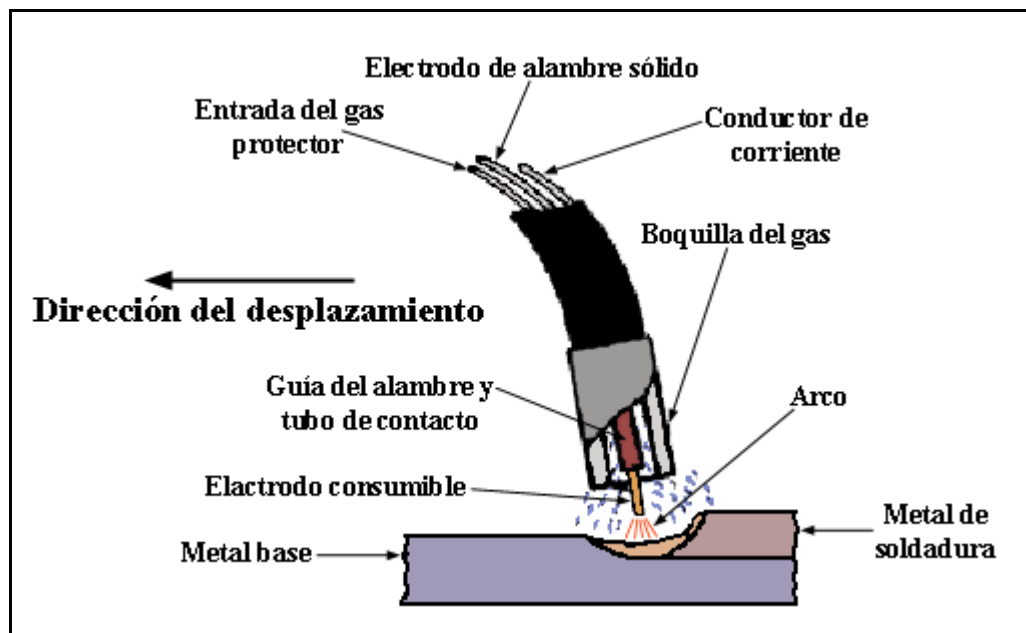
Proceso de soldadura GMAW<sup>(37)</sup>.
